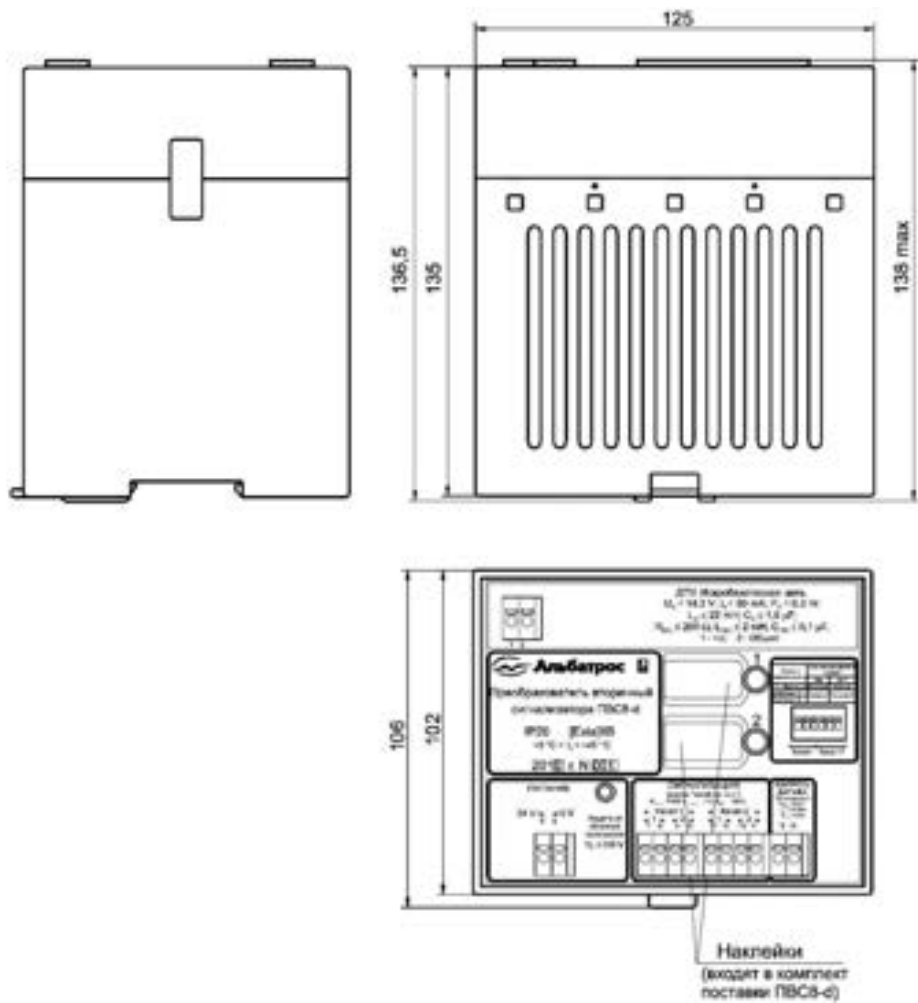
Габаритные размеры вторичного преобразователя ПБСВ-д
